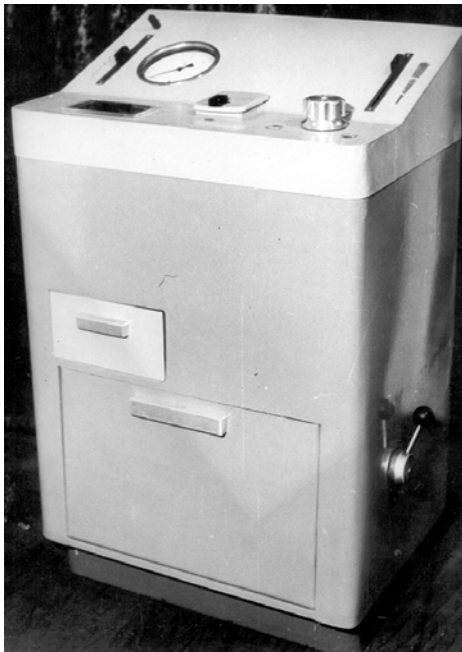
Установка для абразивної обробки затопленими струменями із пневматичним вібратором
